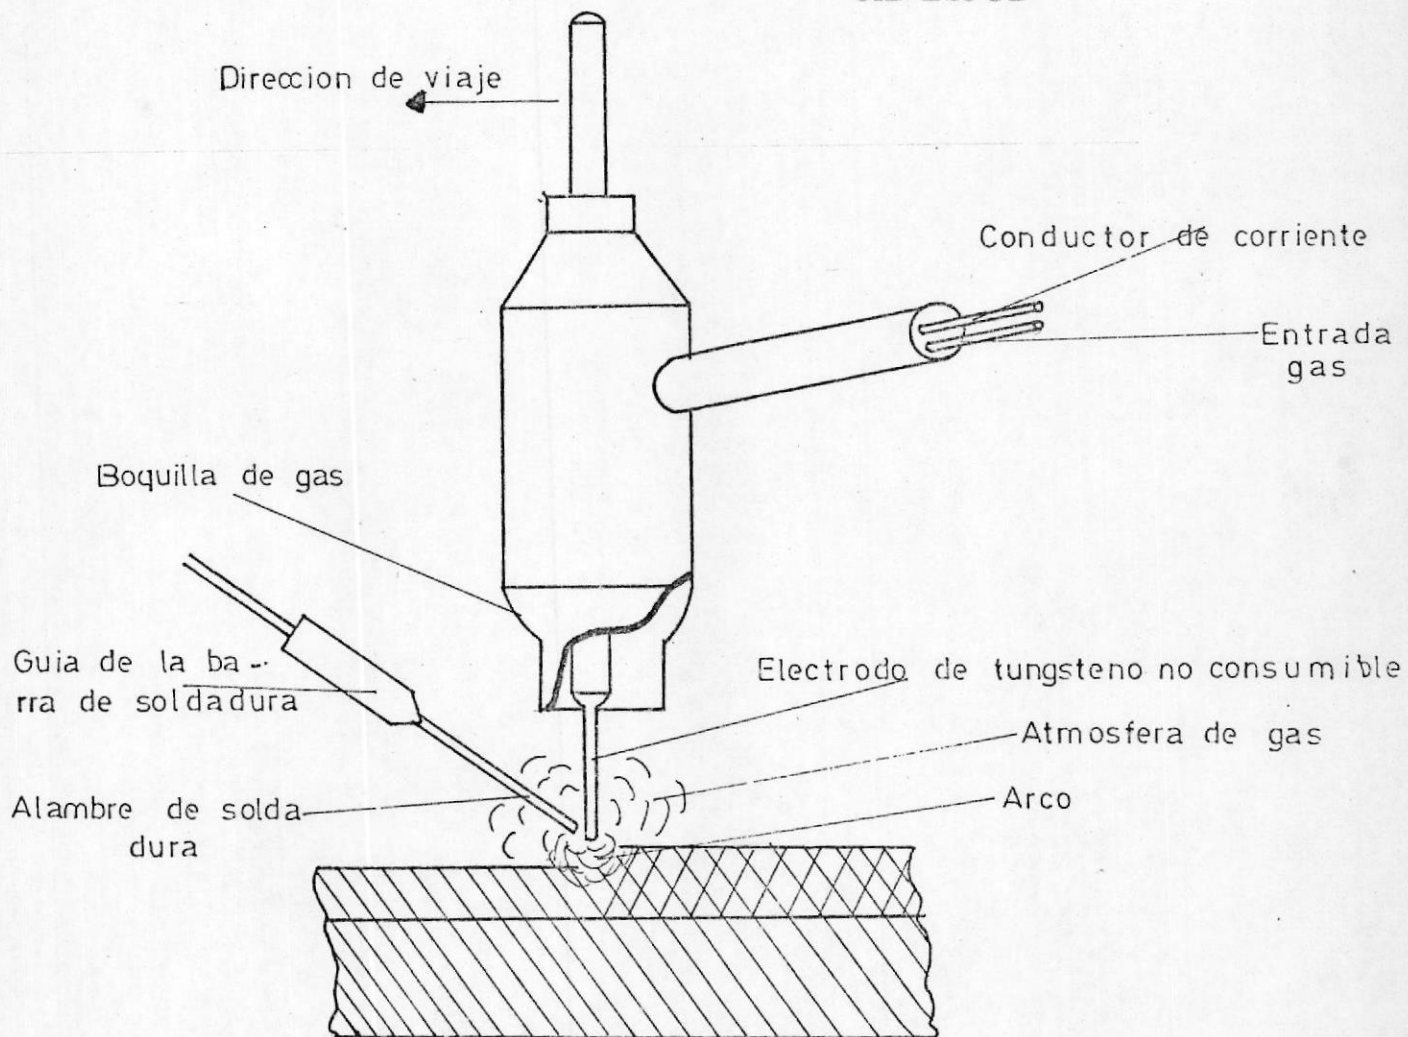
SOLDADURA AL ARCO CON GAS PROTECTOR (6)
